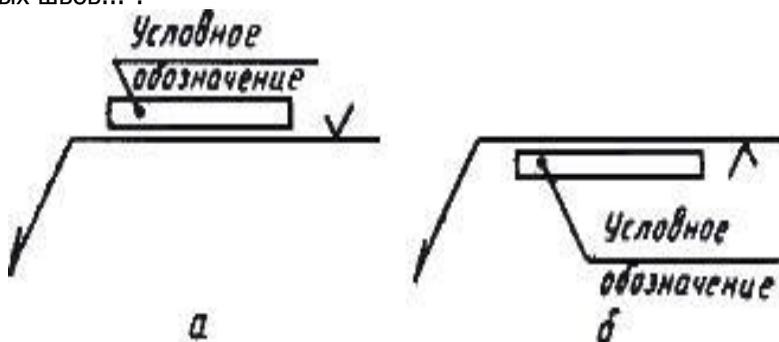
Место обозначения шероховатости механически обработанной поверхности (а – видимый шов, б – невидимый шов)
